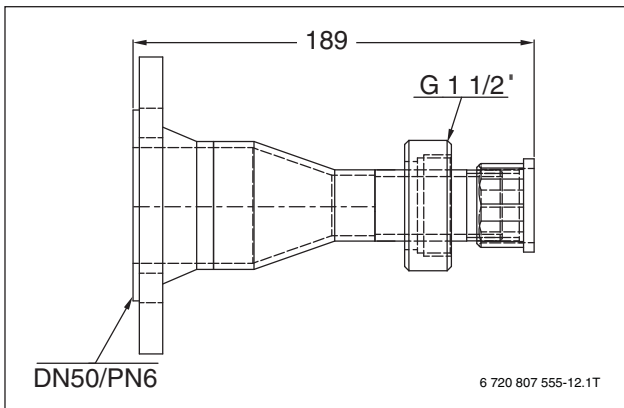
Anschlussstück DN 50/PN 6 – G 1 1/2" (Maße in mm)
